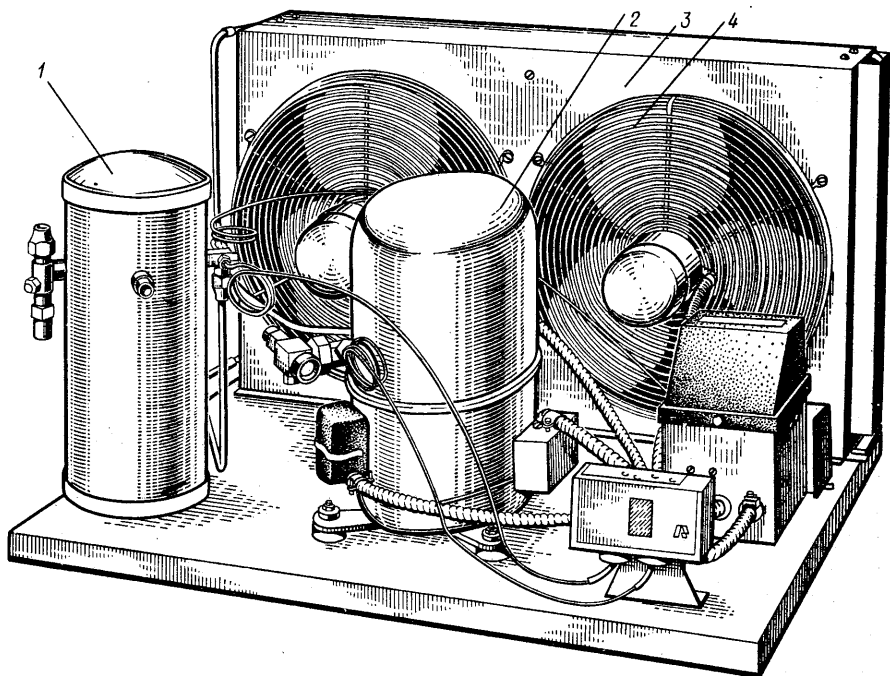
Компрессорно-конденсаторный агрегат с воздушным охлаждением:
